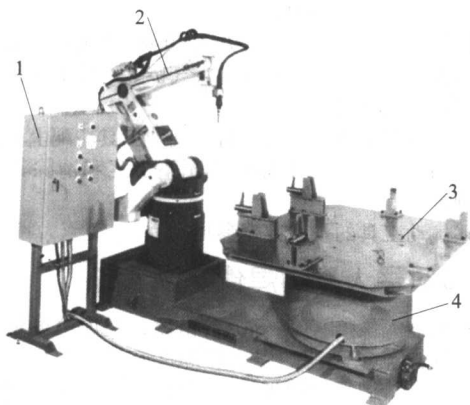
弧焊机器人与水平式焊接回转台
